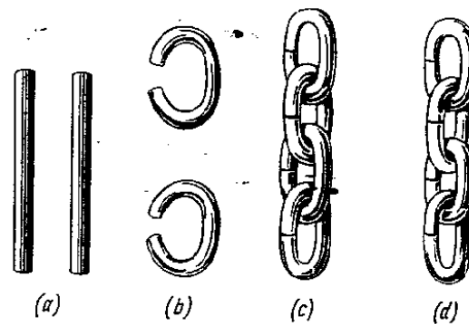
Etapas da fabricação de correntes soldadas
